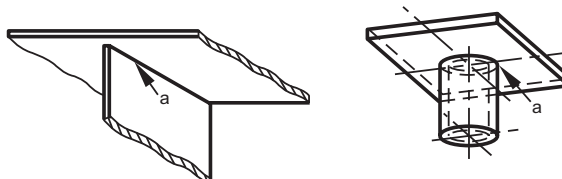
Примеры основных позиций сварки (продолжение)
